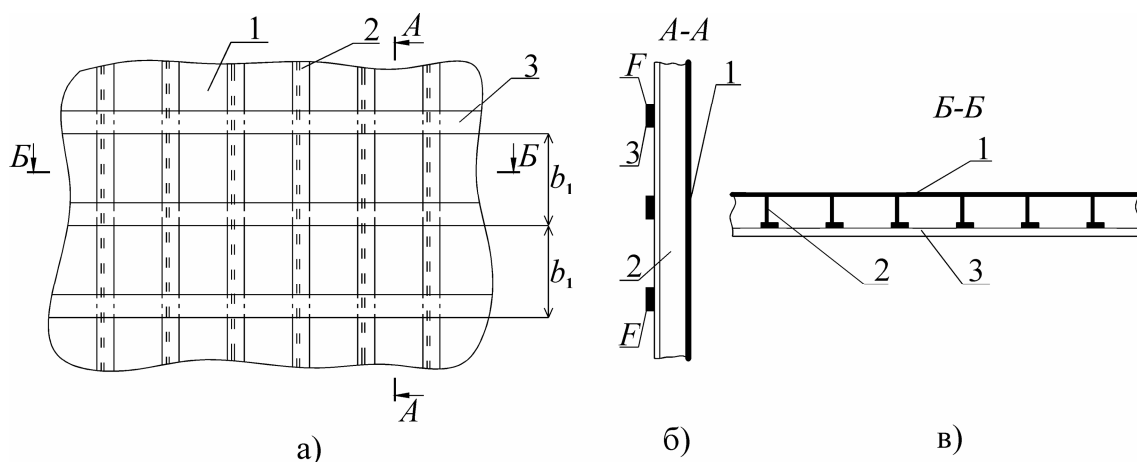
Схема подкрепления шпангоутов при помощи системы струн: а)– общий вид бортового перекрытия; б)– разрез А-А; в)– разрез Б-Б
